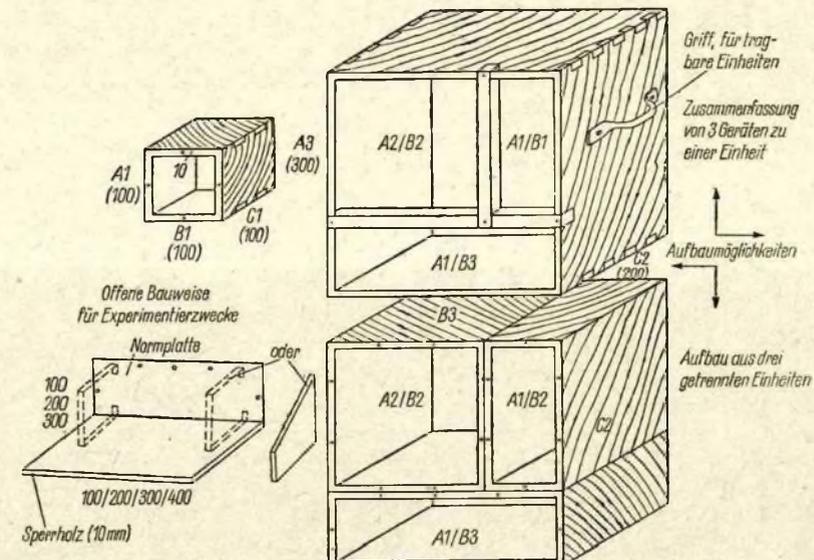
Offene Bauweise für Experimentierzwecke und Holzgehäuse für dekadische Normchassis in Einzelausführung oder kombiniert in einem Holzgehäuse
